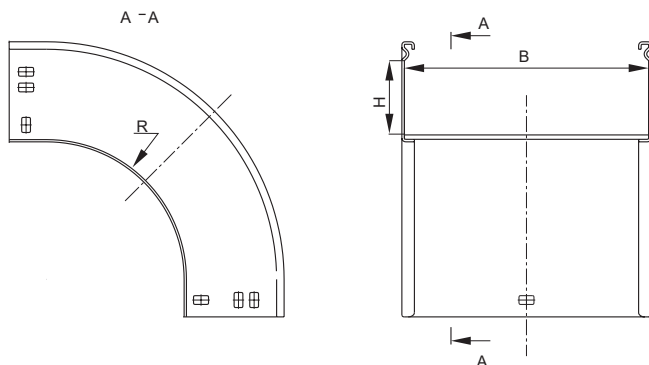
Поворот плавный 90° тип В20. Размеры для размещения кабеля / Figure С.2 – 90° smooth bend В20 type. Dimensions for cable placement
